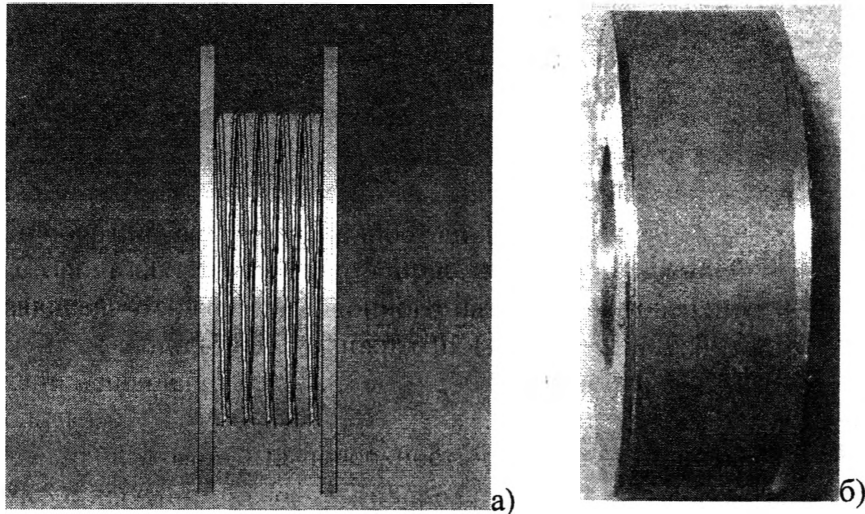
Вид исследуемых образцов: а) - перед покрытием, б) - после нанесения клеевого покрытия и механической обработки
